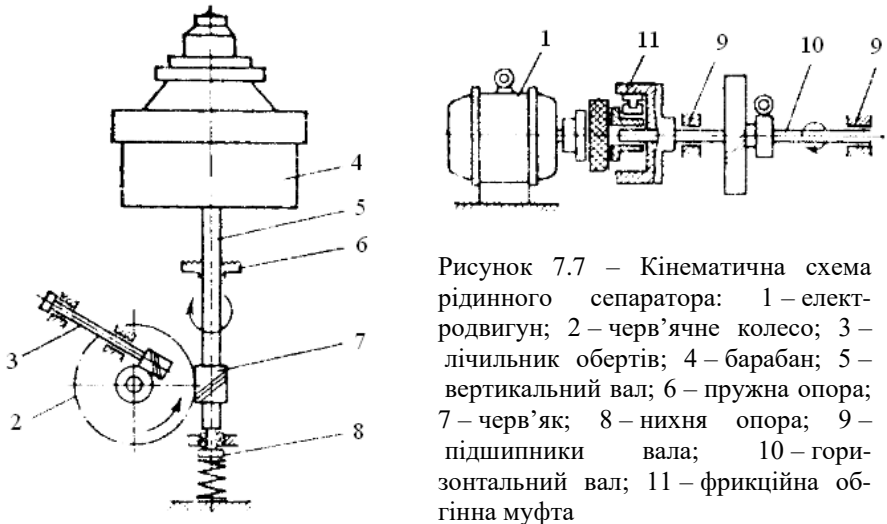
Кінематична схема рідинного сепаратора: 1 – електродвигун; 2 – черв'ячне колесо; 3 – лічильник обертів; 4 – барабан; 5 – вертикальний вал; 6 – пружна опора; 7 – черв'як; 8 – нижня опора; 9 – підшипники вала; 10 – горизонтальний вал; 11 – фрикційна обгінна муфта
